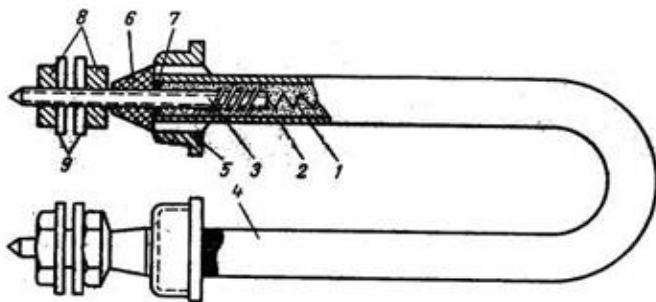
Герметично закритий трубчастий електронагрівач: 1 – спіраль; 2 – стінка трубки; 3 – контактний стержень; 4 – корпус; 5 – штуцер; 6 – електроізоляція; 7 – герметик; 8 – гайка; 9 – шайба.
